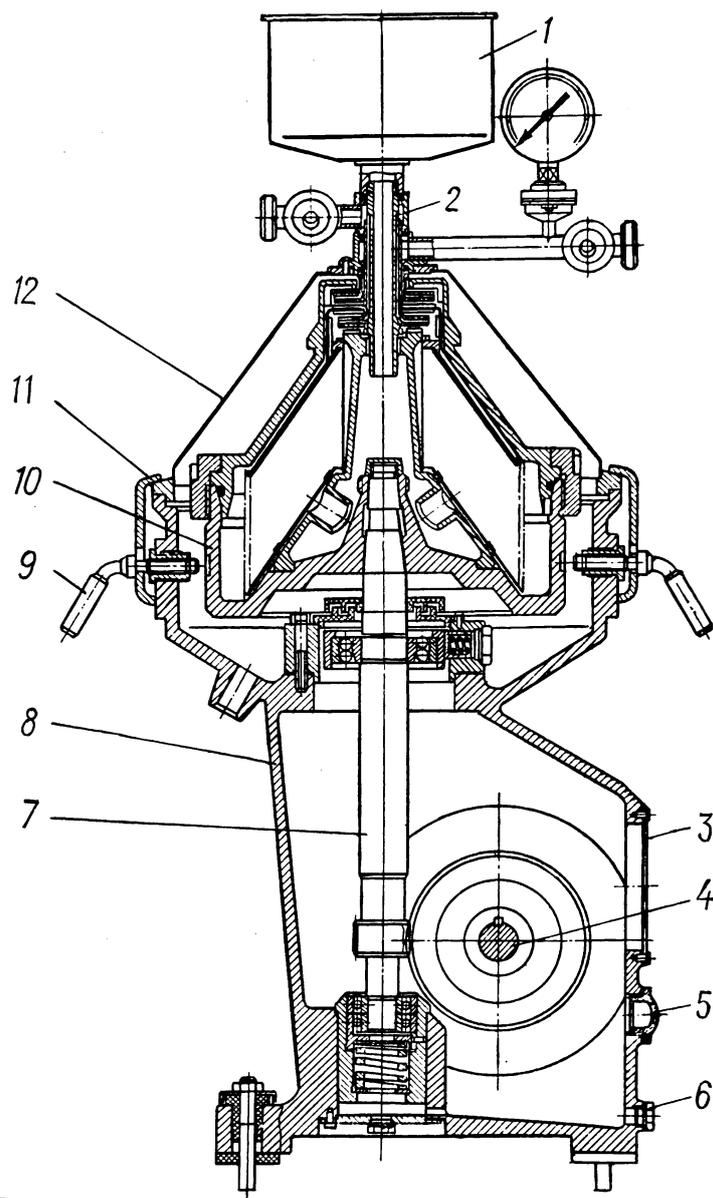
Сепаратор Г9-ОСП: 1 – приемная воронка; 2 – приемно-отводящее устройство; 3 – крышка; 4 – горизонтальный вал; 5 – указатель уровня масла; 6 – пробка спуска масла; 7 – вертикальный вал; 8 – станина; 9 – упорный винт; 10 – барабан; 11 – прижимная планка; 12 – колпак
